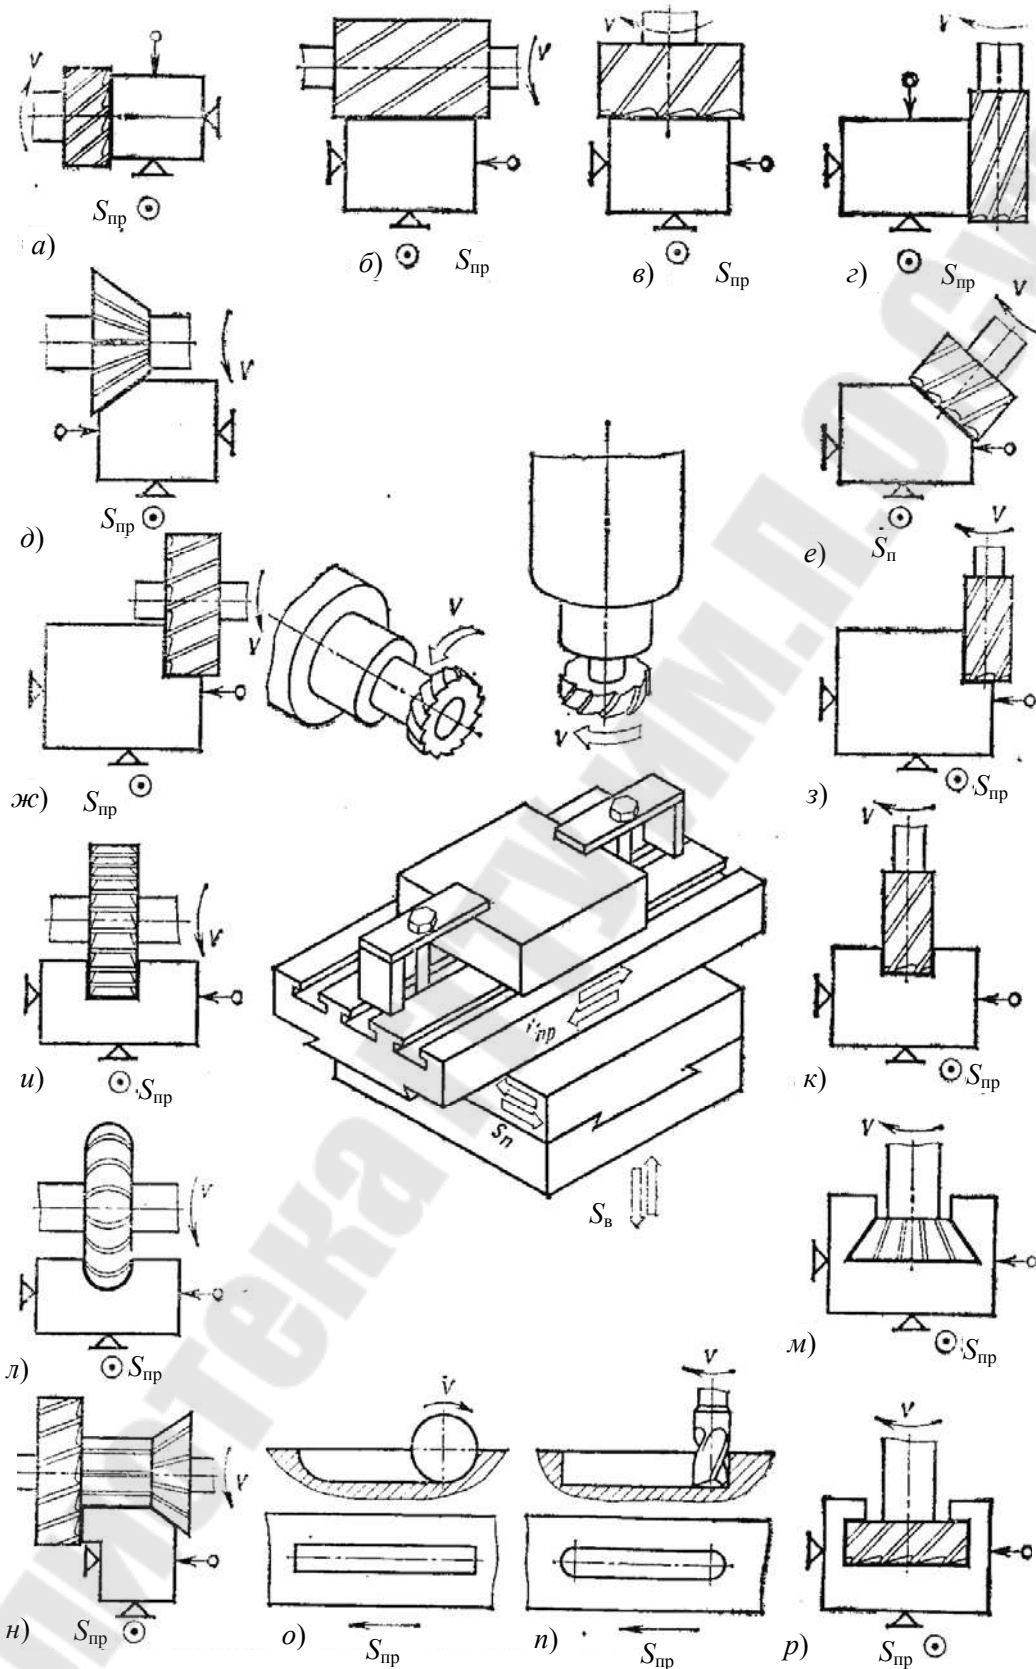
Схемы обработки поверхностей на универсальных фрезерных станках
